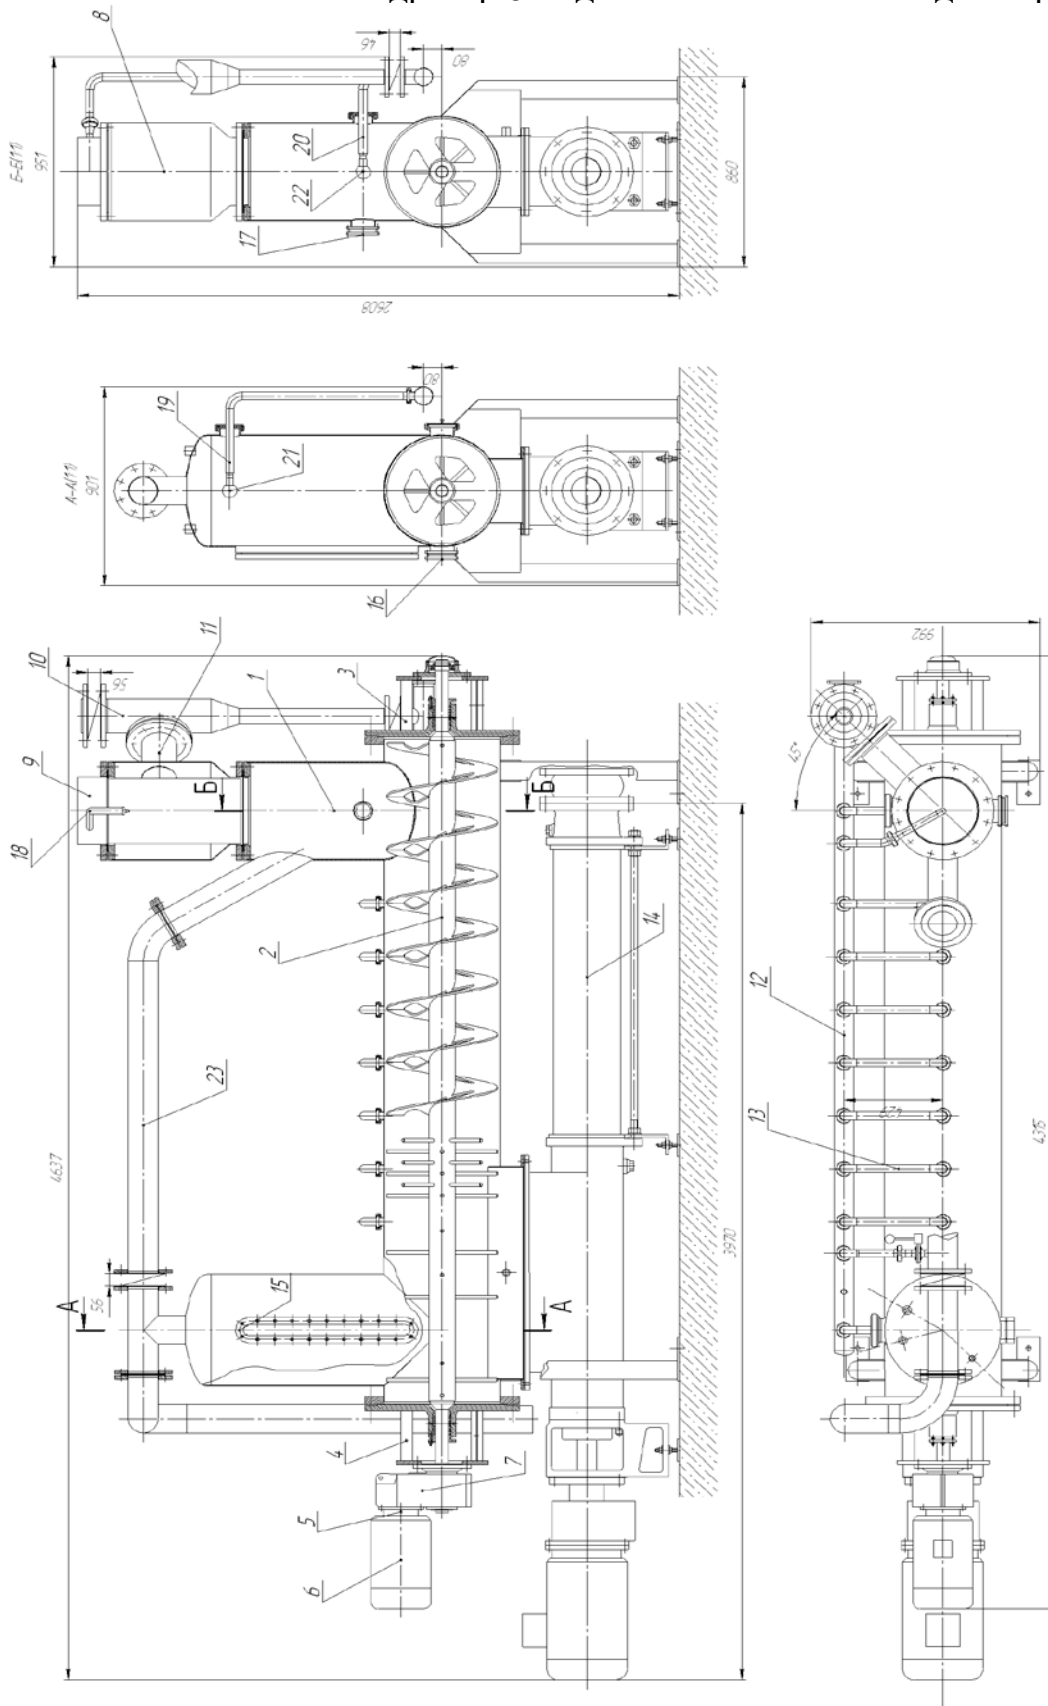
Гомогенізатор подрібненого солоду: 1 – корпус; 2 – гомогенізуючий вал; 3,4 – опори вала; 5 - привод; 6 - електродвигун; 7 – редуктор; 8 - гідратор; 9 – патрубок для подачі крупки; 10 – труба для подачі води; 11 - з'єднувальний патрубок; 12 – розподільча труба; 13 – патрубок; 14 – хвильвий насос; 15,16,17 – оглядові вікна; 18 – патрубок для подачі води; 19,20 – патрубки для миття «СП»; 21,22 – сферичні форсунки; 23 – труба для видалення
